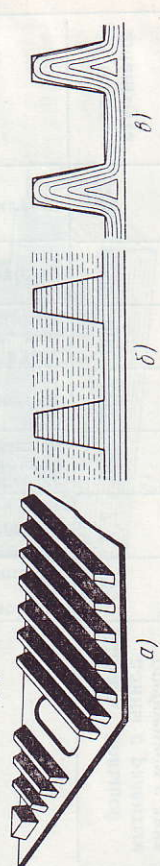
Панель с поперечным оребрением (а); сечения панелей, полученных фрезерованием катаной плиты (б) и из штампованной поковки (в) [49]
